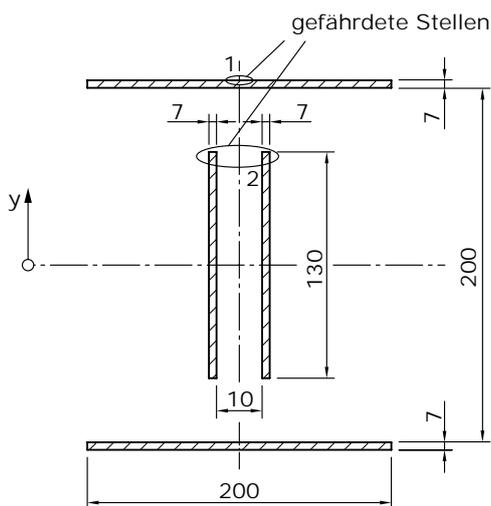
Anschlussfläche Schweissnähte (B809sWSZ)
